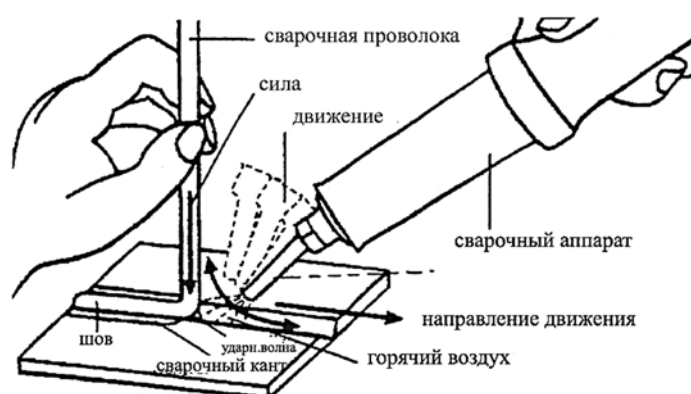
Процесс сварки пластмасс нагретым газом
